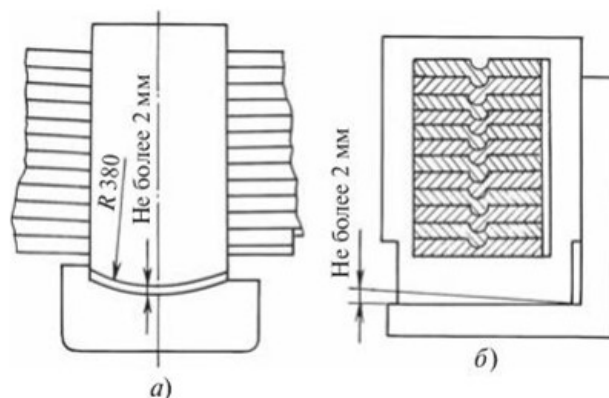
Схема проверки опорной поверхности хомута рессоры
